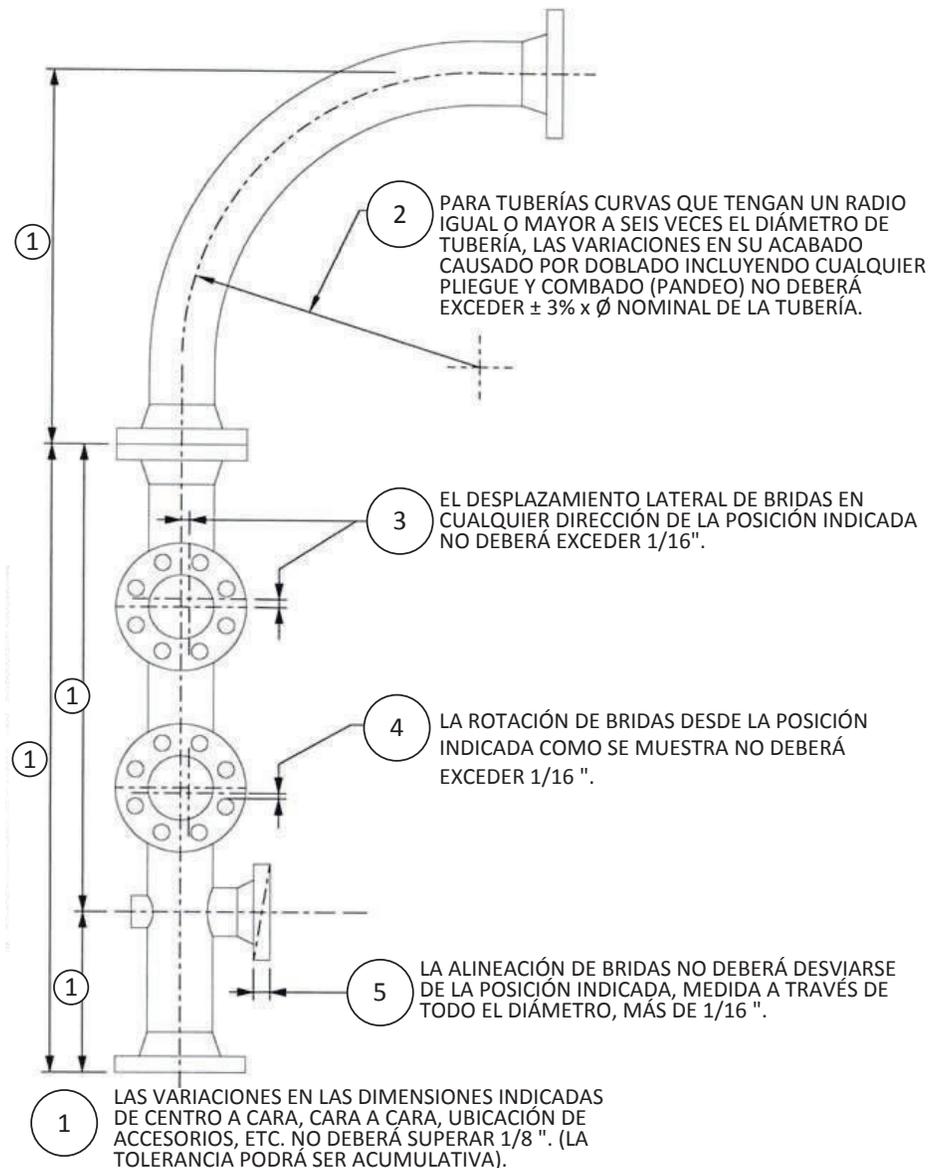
Tolerancias para fabricación de tubería, recomendadas por el Pipe Fabrication Institute.
